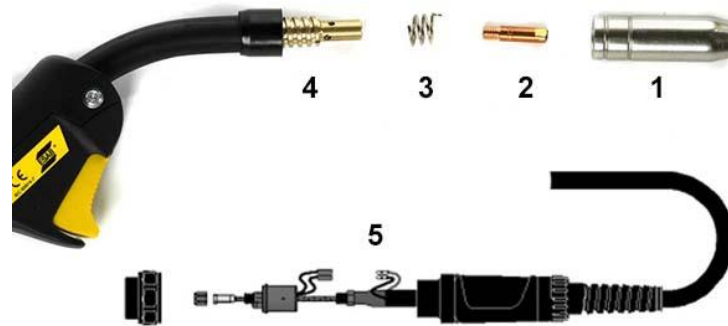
Зварювальний пальник ESAB MXL 180 для MIG/MAG зварювання
